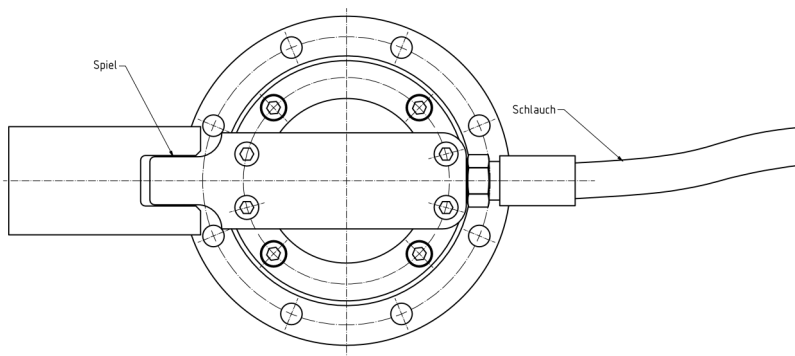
Beispiel für Drehmomentstütze mit Gewindebohrungen am Umfang.
